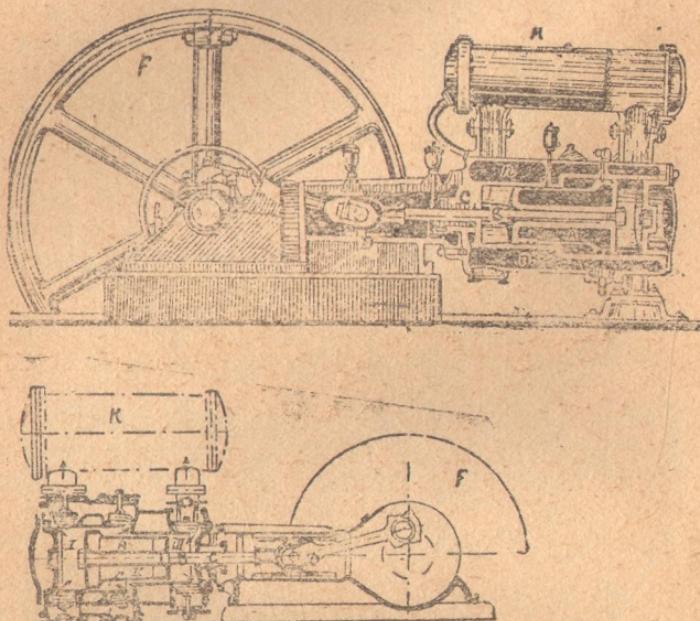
а. Разрез двуступенчатого двухцилиндрового компрессора
